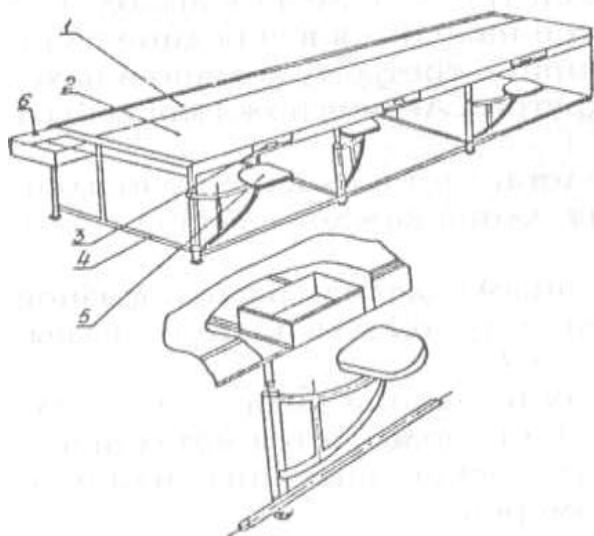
Стол для разделки тестовых заготовок:
